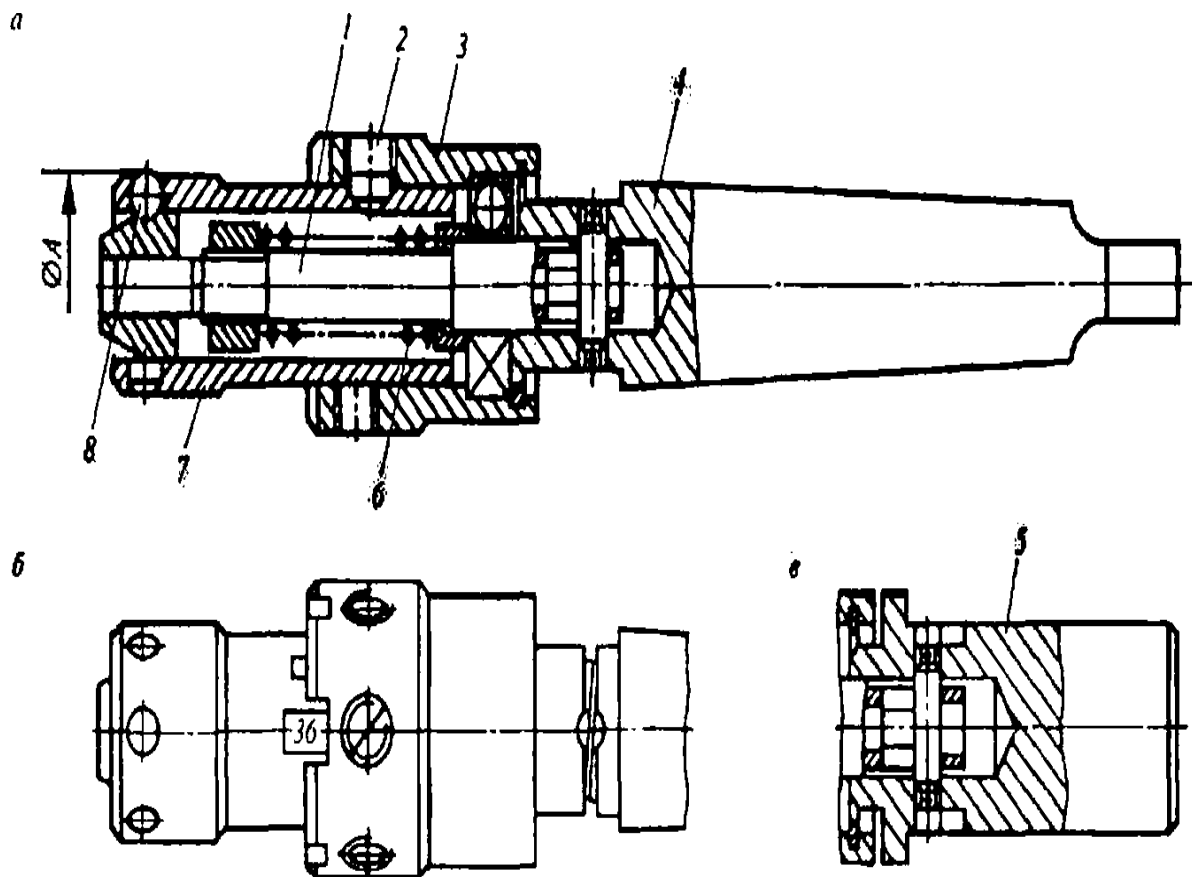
Рельсовый раскатник: а, в — разрез; б — внешний вид
